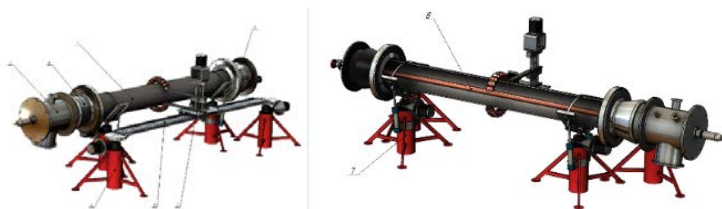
Внешний вид устройства для вакуумного напыления внутренних поверхностей протяженных цилиндрических изделий:
